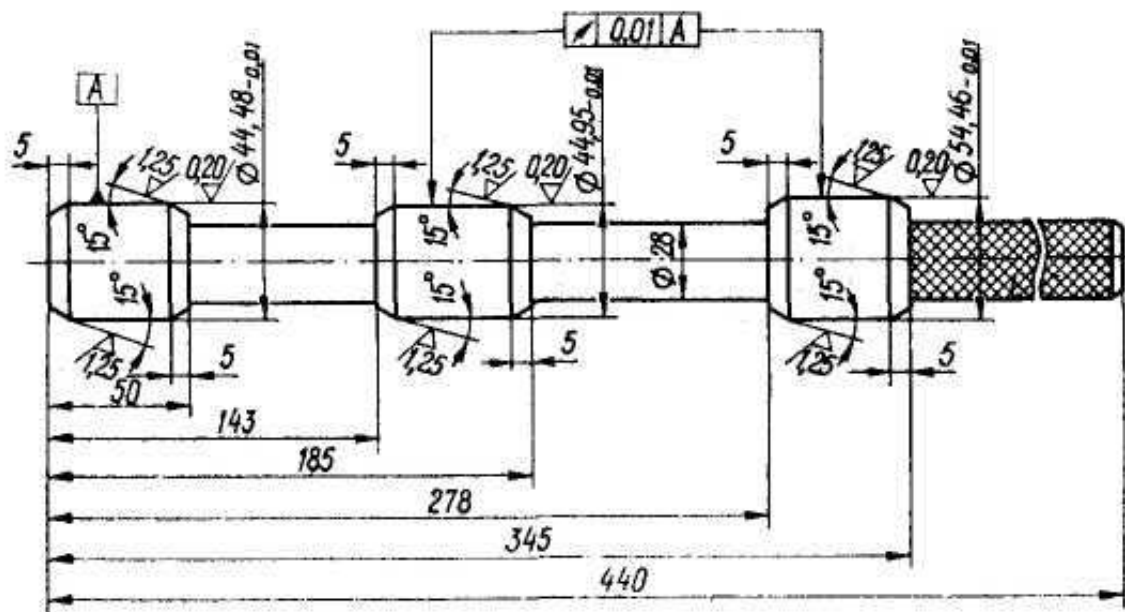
Оправка для проверки соосности подшипников распределительного вала
